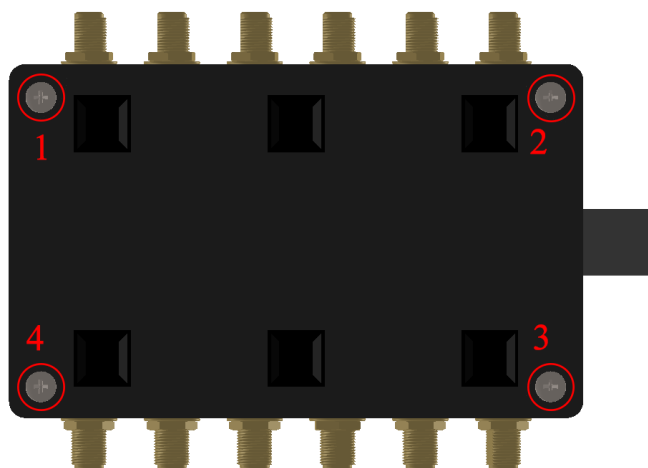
Розташування чотирьох гвинтів М3 для корпусу
